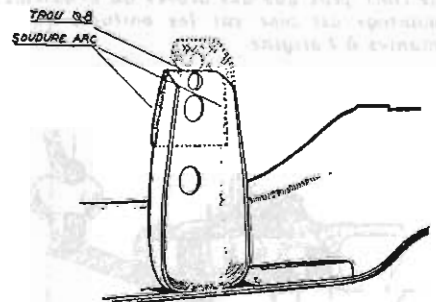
Vue de face du support. En pointillé : partie à couper.
